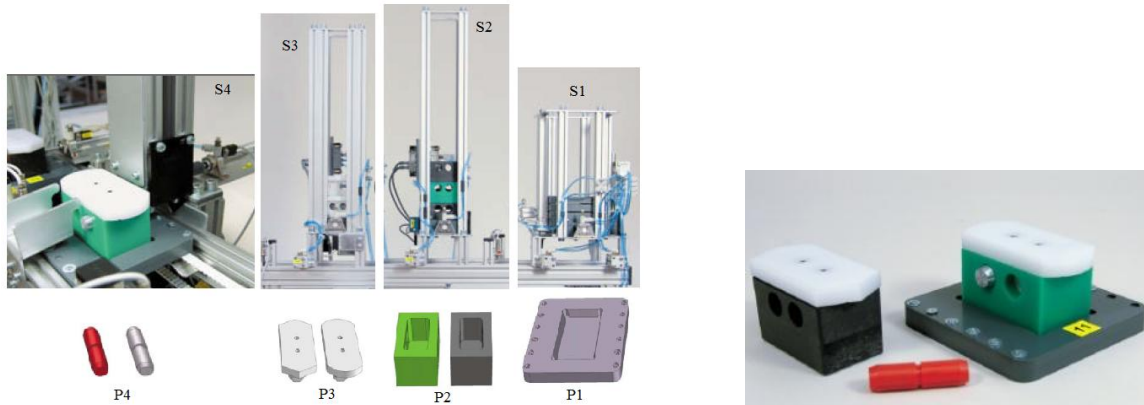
a) Stațiile de asamblare/dezasamblare și componentele aferente acestora; b) Produs final
